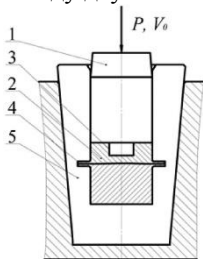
Схема изготовления биметаллического инструмента с формообразующей полостью
